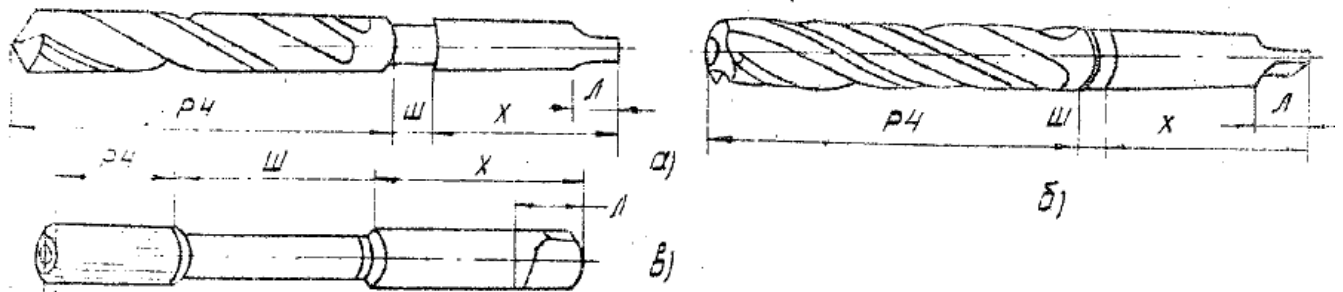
Основные части сверла (а), зенкера (б) и развертки (в)
